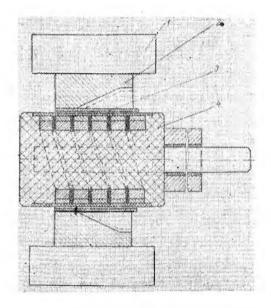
Схема процесса раздачи тоубчатых заготовок энергией ИМП 1— губки зажимных тисков; 2— матрица; 3—заготовка; 4— индуктор
